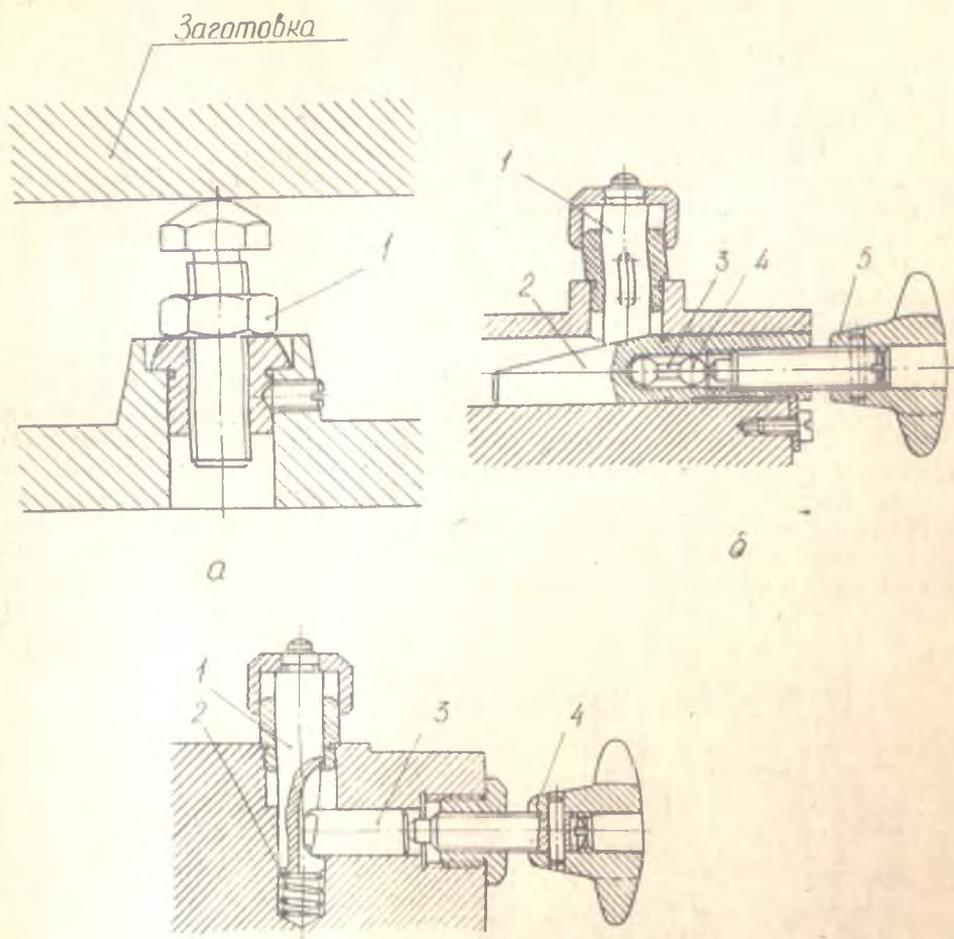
Конструкции вспомогательных опор: а — винтовая; б — подводимая клиновья; в — самоустанавливающаяся, пружинная
